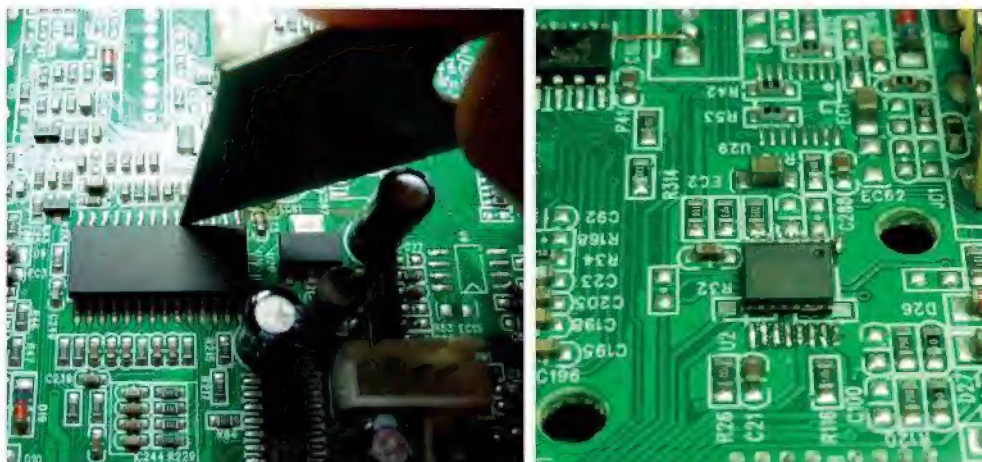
Découpe au cutter des broches de circuits intégrés
